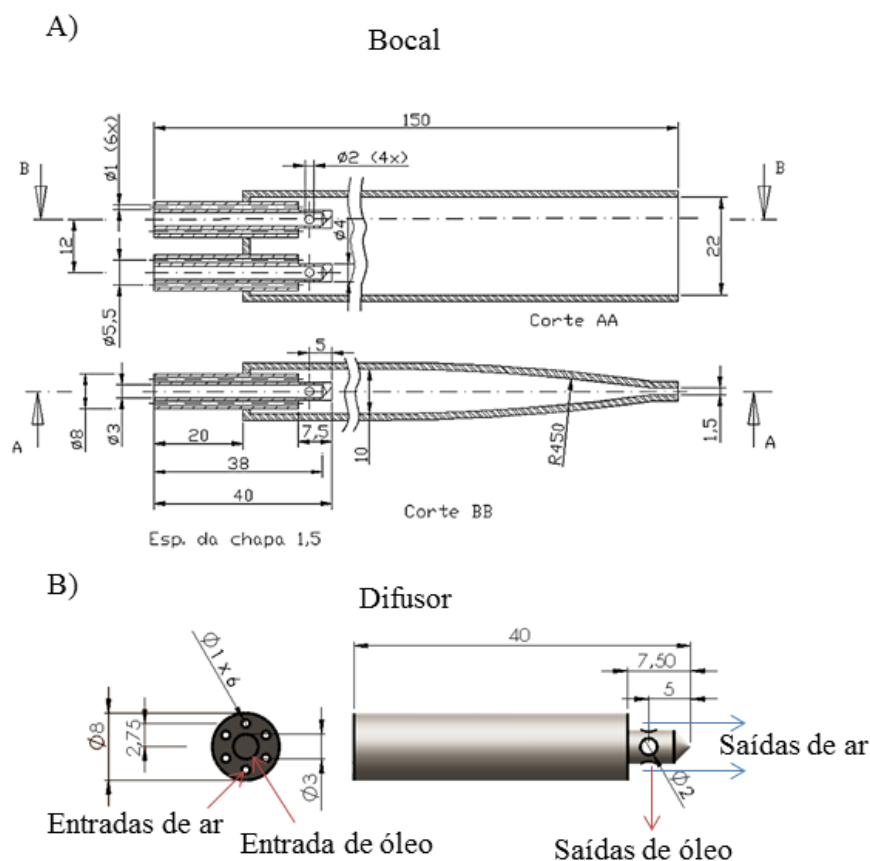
Desenho do bocal utilizado na técnica MQL (BELENTANI et al., 2014), modificada.
